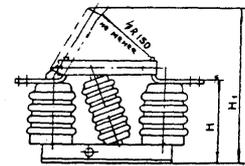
Разъединитель трехполюсный типоразмера РВФ 310/630-1000 II-II УХЛ2
